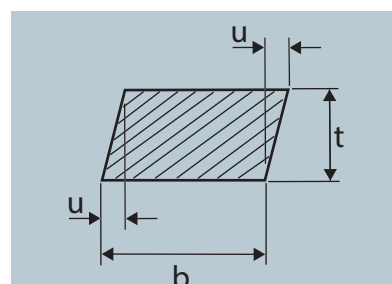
Warmgewalzter Flachstahl: Abweichung von Rechtwinkligkeit
